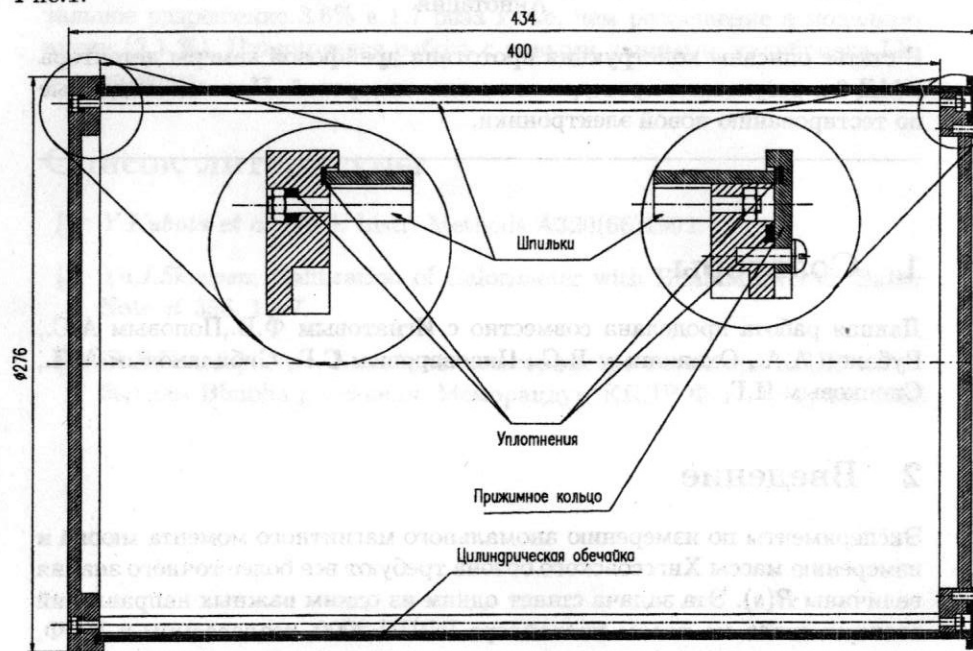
Сборочный чертеж макета дрейфовой камеры.
